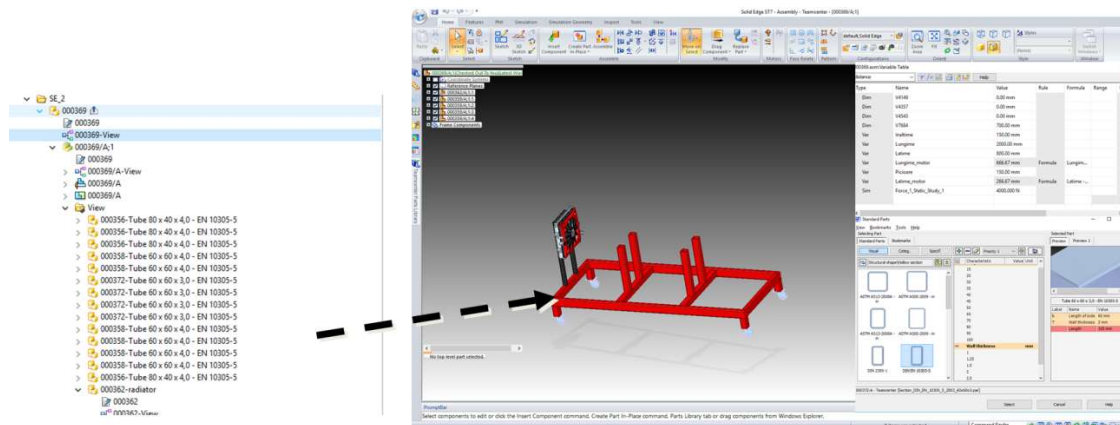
Integrare Siemens SolidEdge ST7 – Siemens Teamcenter
